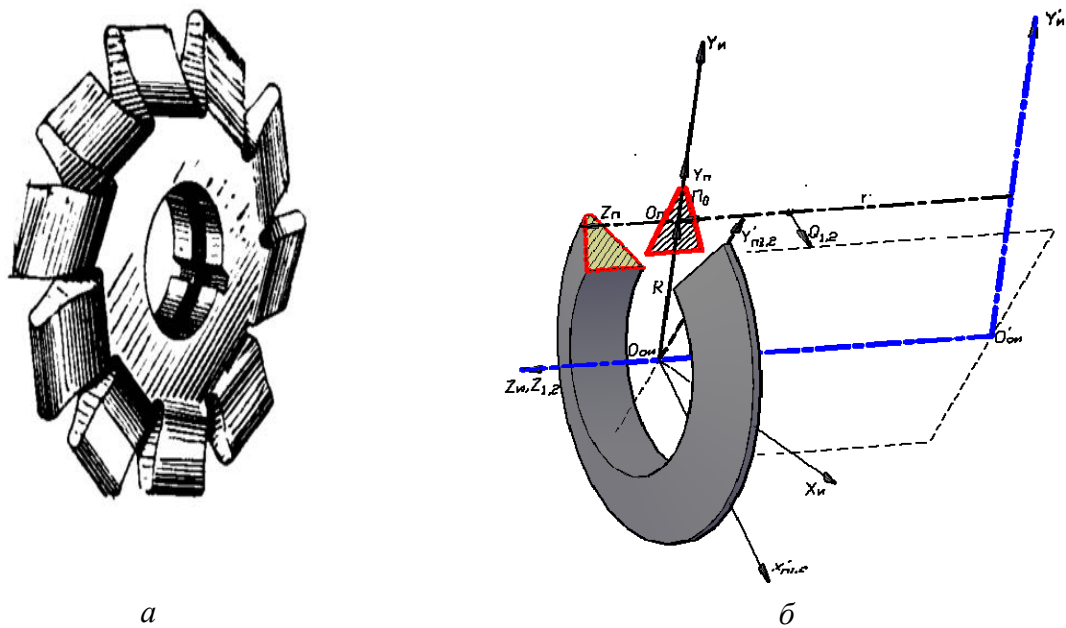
Зуборезный инструмент «дисковая фреза»:
